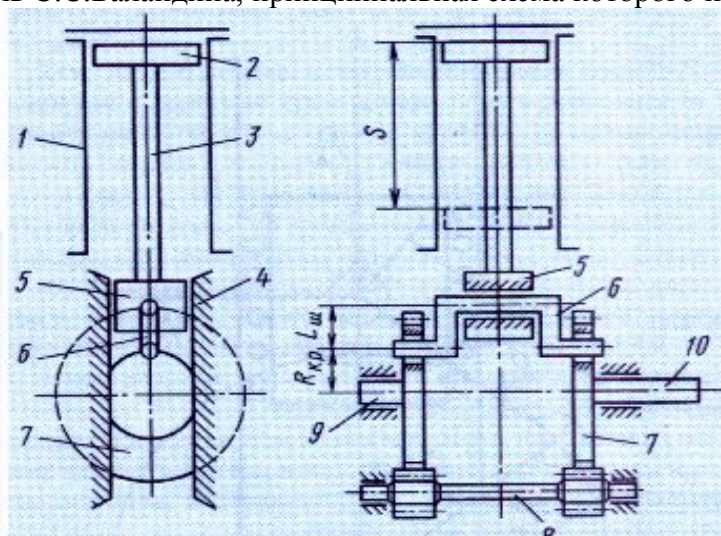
Схема одноцилиндрового модуля механизма Баландина:
